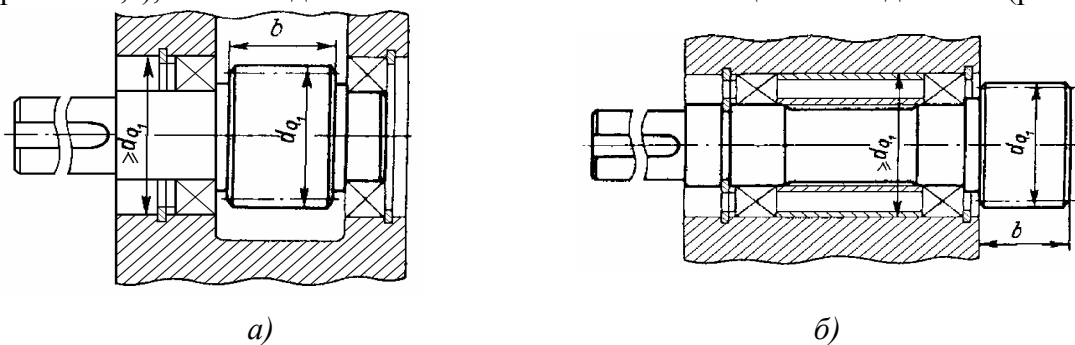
Неплавающие центральные колеса с наружными зубьями
